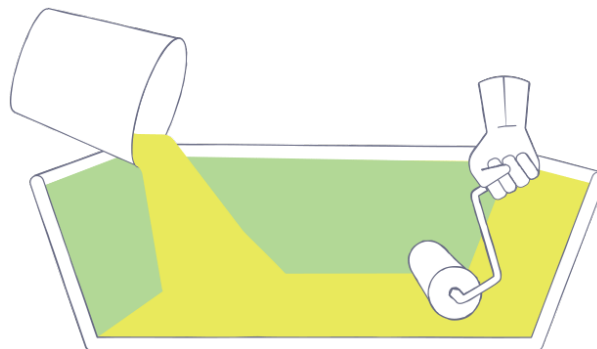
Wet layup* com molde, *Wet Hand Layup Molding* (n.d.).
